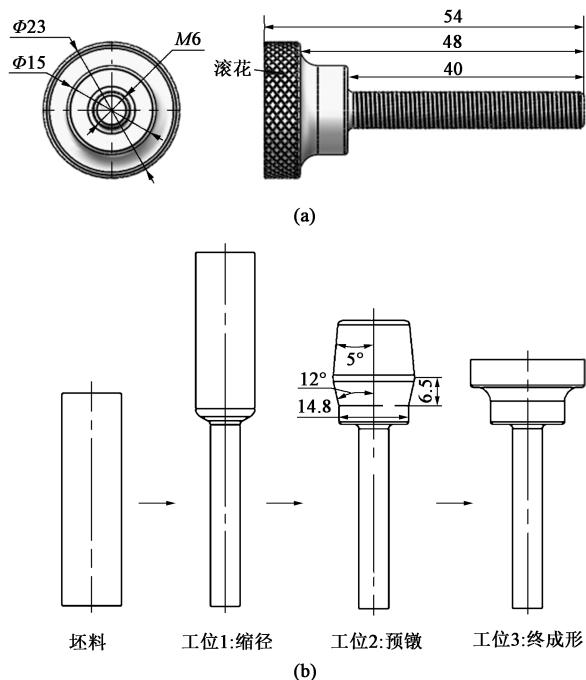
手柄螺丝零件图 (a) 及成形工艺 (b)
